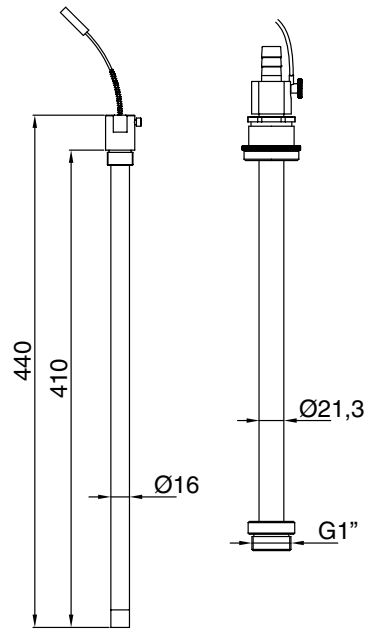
Sonde et tube d'aspiration, pompe à piston LA 3XX montage mural
